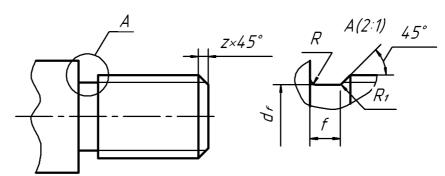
Проточка и фаска наружной метрической резьбы
